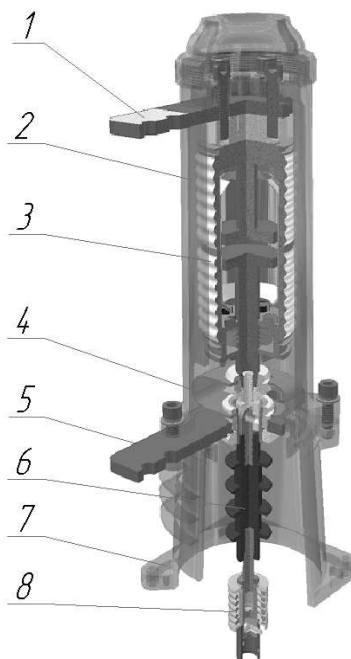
Вакуумный выключатель типа ВВУ-СЭЩ-ЭЗ-10-20/1600
